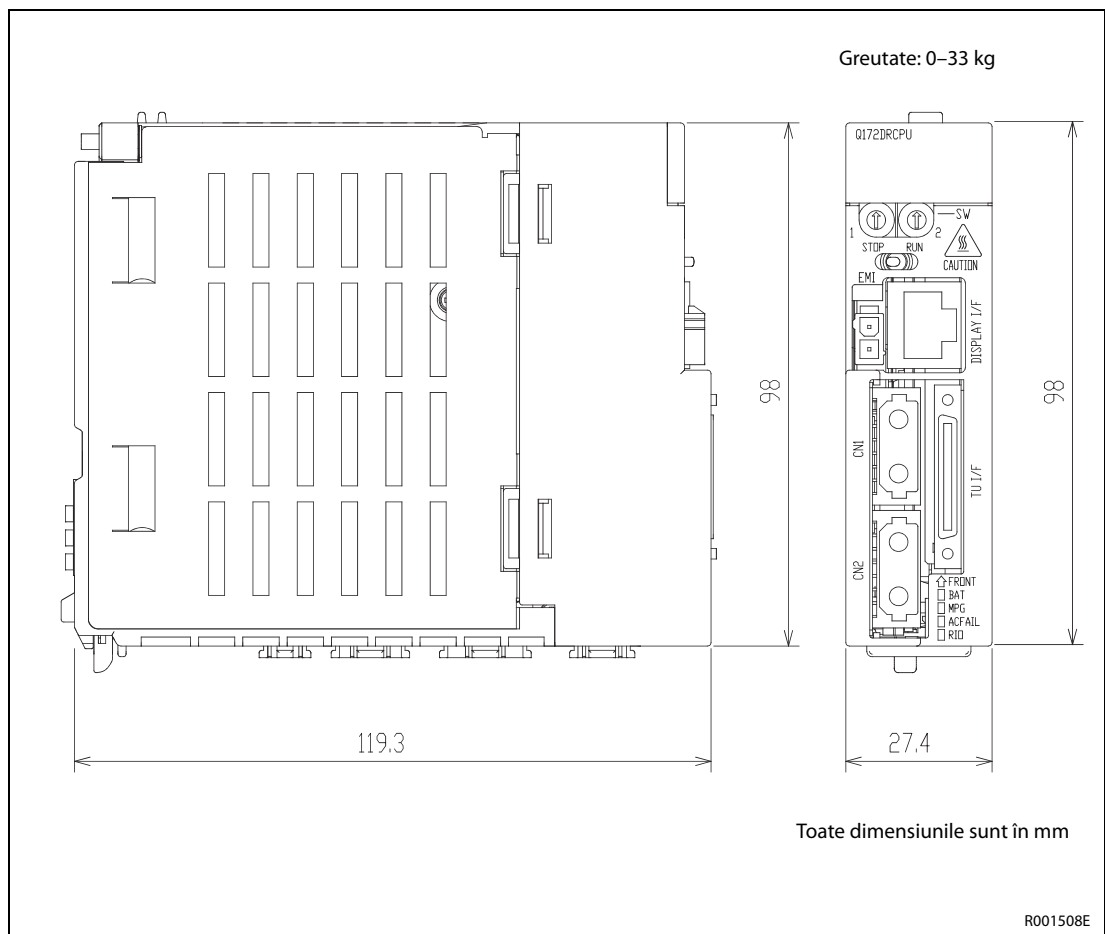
Dimensiunile modulului CPU Robot Q172DRCPU
